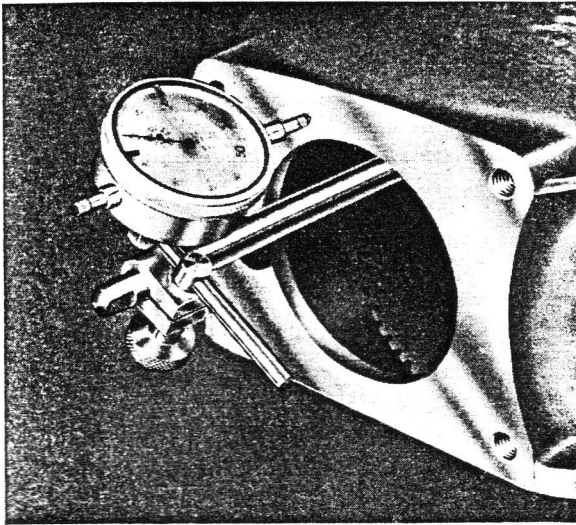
Schwungradgehäuse mit Messuhr ausmessen
